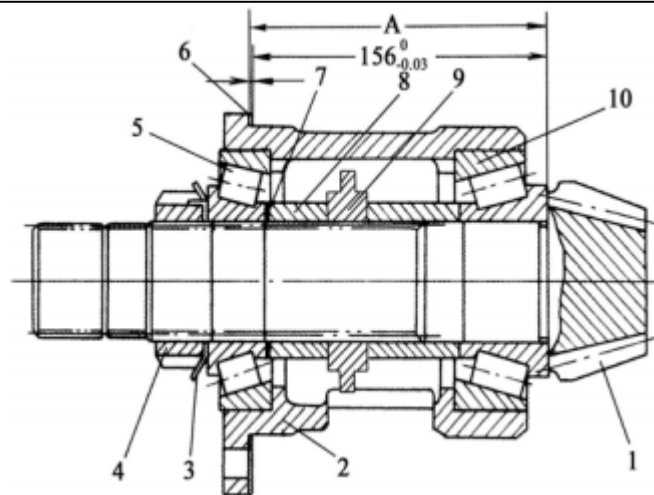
ajuste de los rodamientos del eje de engranajes cónicos pequeños
